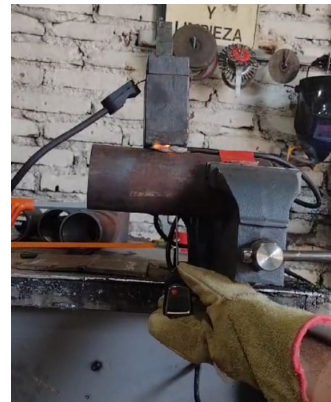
Medición de Temperatura antes y durante el Proceso de Soldadura
